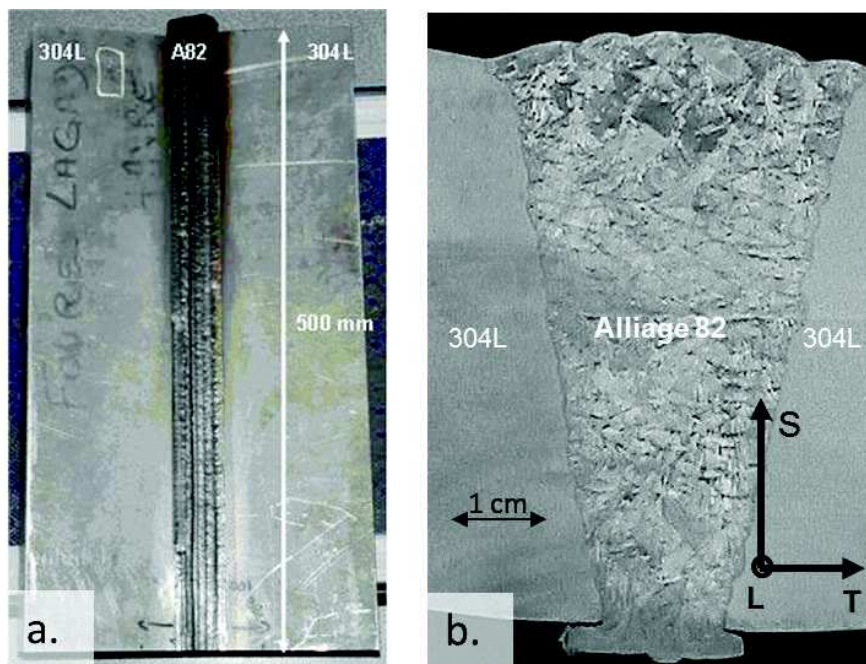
Vue (LT) d'un moule de soudure (a.) et vue en coupe d'un moule obtenue en microscopie optique après polissage mécanique (b.)
